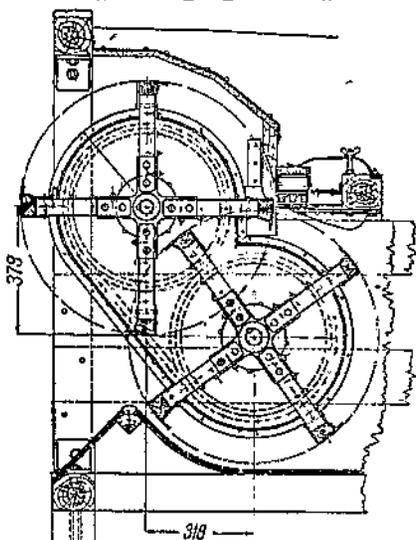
б. Общий вид КЛТ ВНИИЛ-С (вид сверху)
